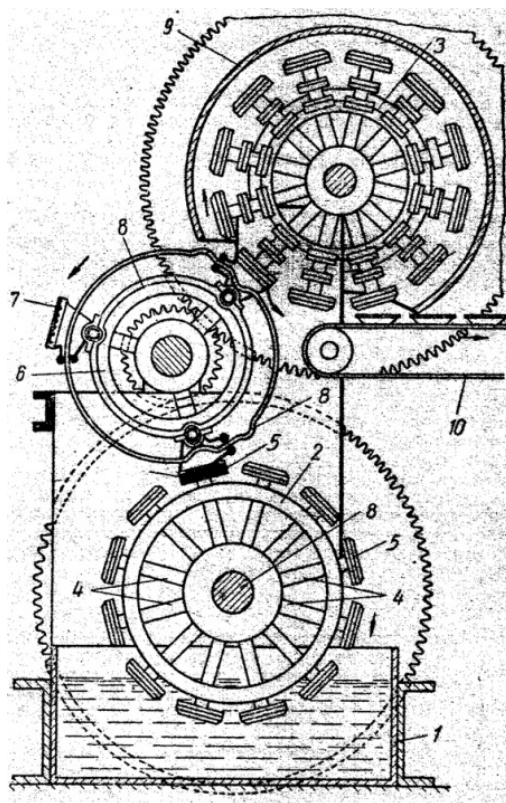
Схема отливной машины для формирования тонкостенных изделий открытой формы с применением вакуума: 1 – ванна с жидкой массой; 2 – формующий барабан; 3 – верхний барабан; 4 – штуцеры для подвода вакуума и воздуха; 5 – сетчатые формы; 6 – пересъемный вал; 7 – сетчатые контр-формы; 8 – криволинейная направляющая; 9 – кожух; 10 – транспортер
